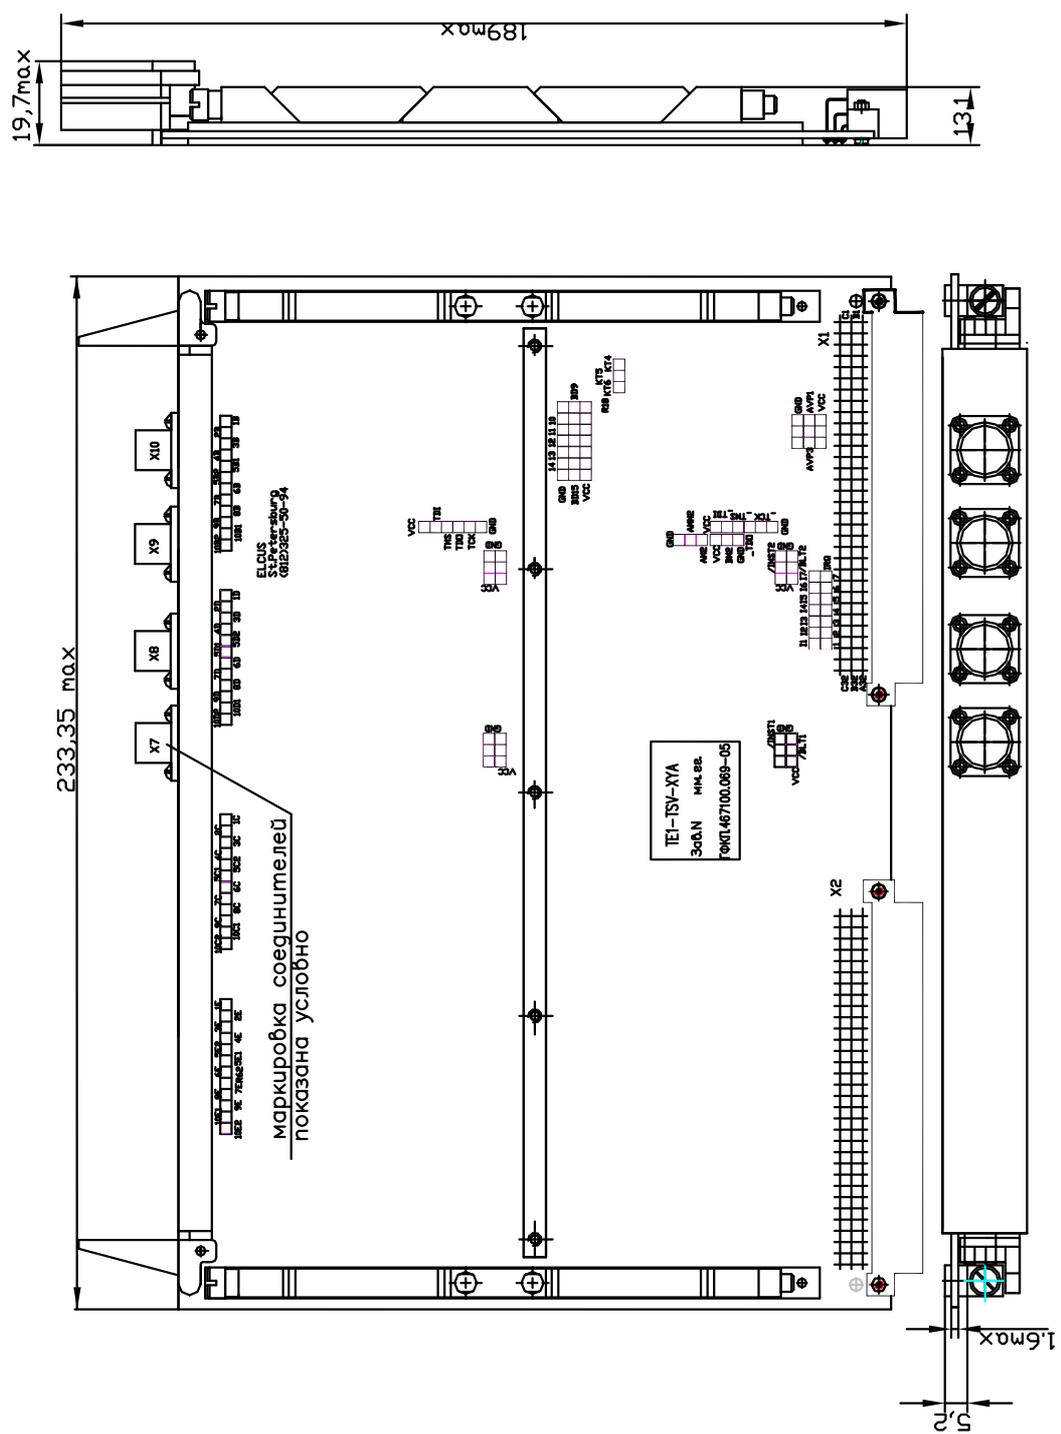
Габаритный чертеж модуля TE1-TSV-2R
